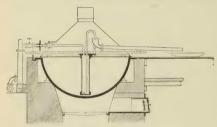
Entsilberungskessel mit Rösings Bleipumpe.
